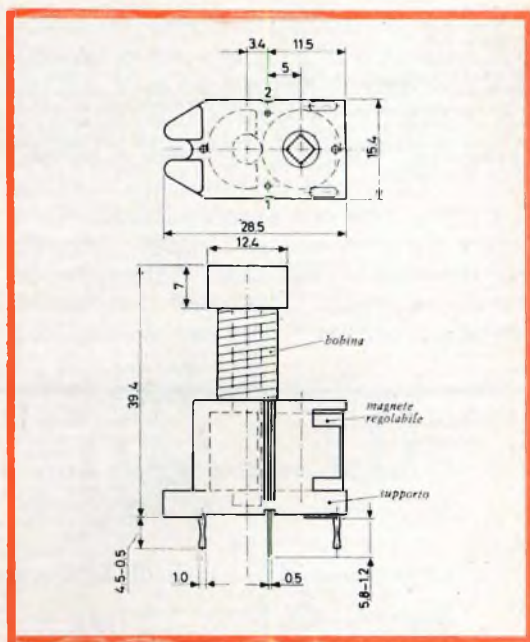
Dimensioni d'ingombro del regolatore di linearità AT 4042/02 n. G.B.C. MG/0598-04.
